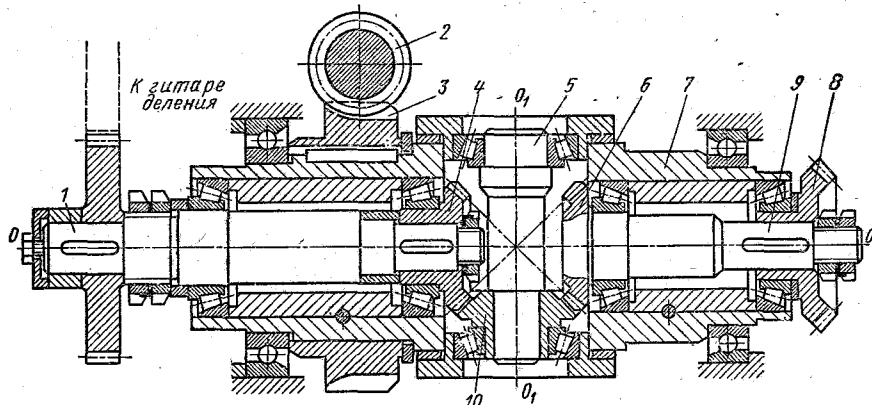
Дифференциал зубофрезерного станка мод. 5К32
